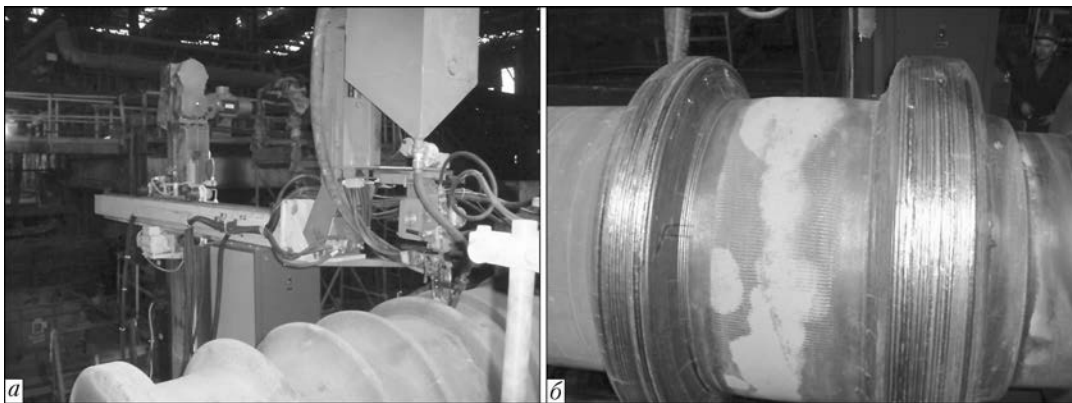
Установка РМ-11 для наплавки прокатных валков заготовительных станков (а) и фрагмент наплавленного прокатного валка (б)
